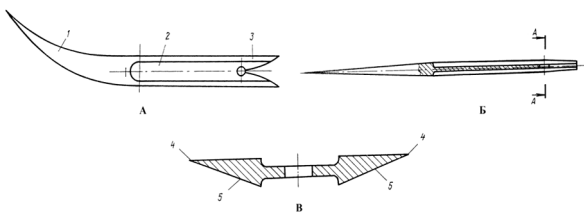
Внешний вид иглы хирургической: 1 — изогнутый рабочий конец; 2 — хвостовик; 3 — захватывающие губки; 4 — угольные режущие кромки; 5 — односторонний скос.
